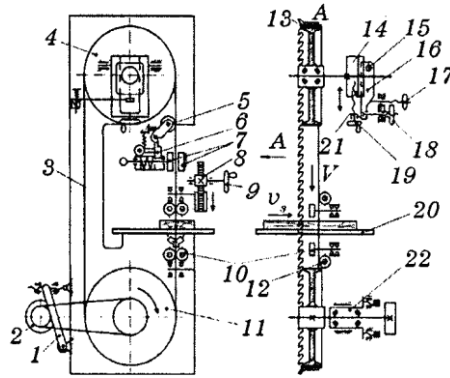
Схема столярного стрічкопилкового верстата: 1 – підмоторна плита; 2 – електродвигун; 3 – пилка стрічкова; 4 – шків натяжний; 5 – ролик контактний; 6 – храповик; 7 – гальмівні колодки; 8 – зубчасто-рейкова передача; 9 – маховик; 10 – бокові напрямні ролики; 11 – шків нижній приводний; 12 – упорний ролик; 13 – бандаж; 14 – повзун; 15 – вісь; 16 – кронштейн; 17, 18, 19 – маховички; 20 – робочий стіл; 21 – натяжна пружина; 22 – чаша
